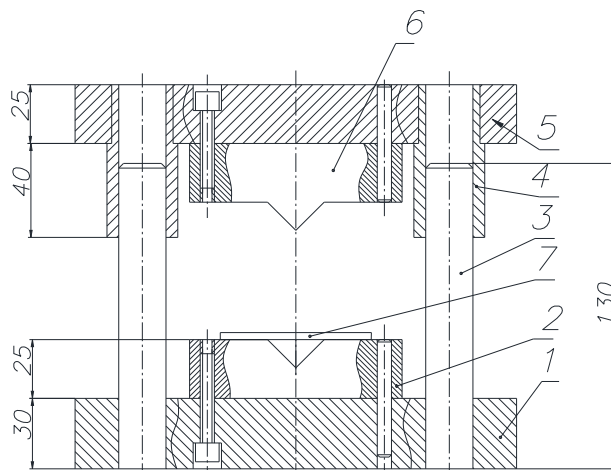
Экспериментальный штамп для гибки: 1-нижняя плита; 2-матрица; 3-колонка; 4-направляющая втулка; 5-верхняя плита; 6-пуансон; 7-заготовка
